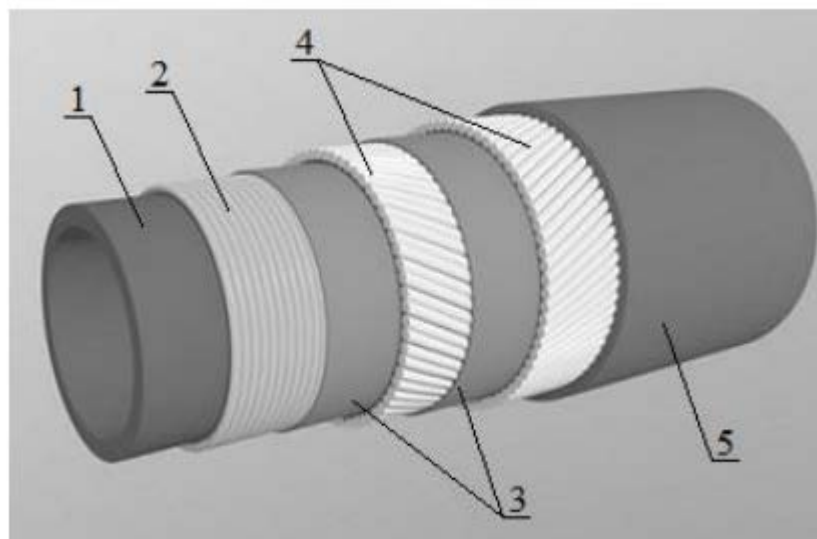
Общий вид гибкой полимерно-металлической трубы:
